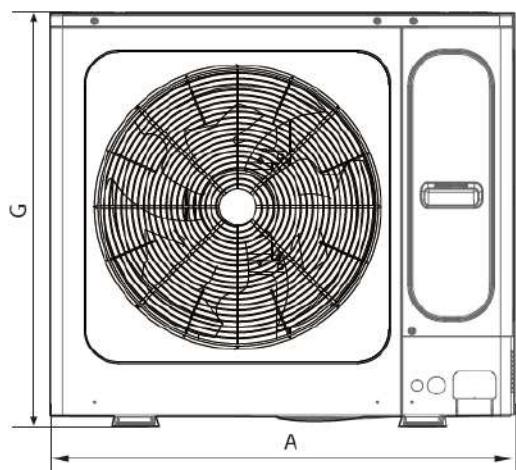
Dimensiones de la vista frontal del Modelo 60
